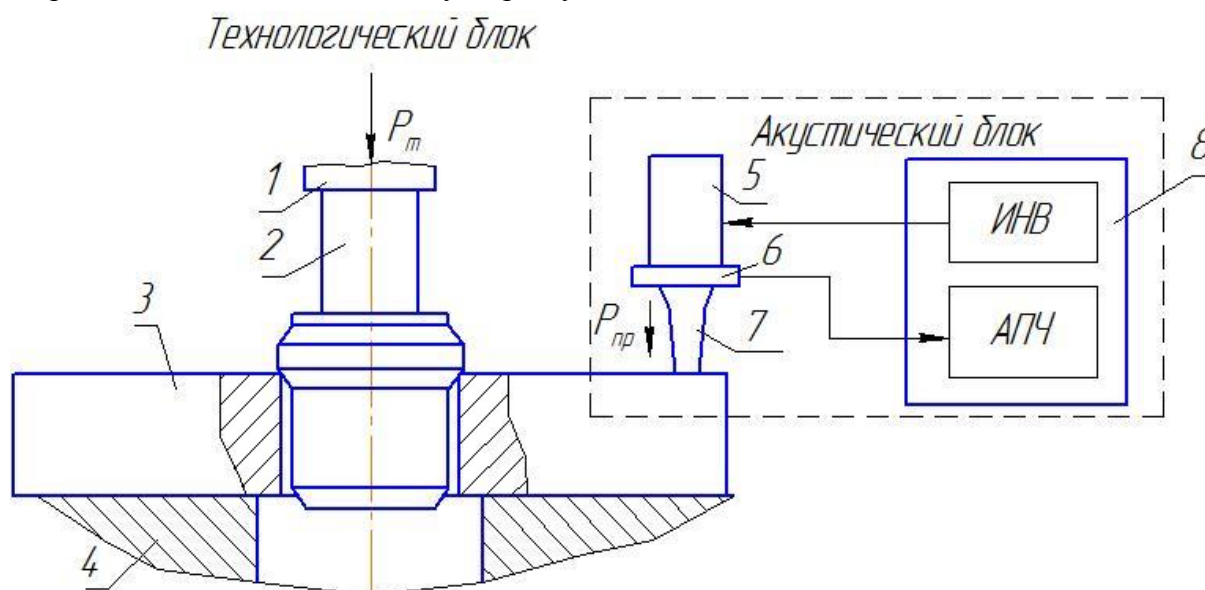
Схема процесса дорнования шлицевого отверстия зубчатого колеса с применением ультразвукового поля: 1-силовой шток, 2- фасонный дорн, 3-зубчатое колесо, 4-, установочный стол, 5- магнитострикционный преобразователь, 6-датчик акустической обратной связи, 7- волновод, 8 – генератор (АПЧ-система автоподстройки частоты, ИНВ- инвертор)
